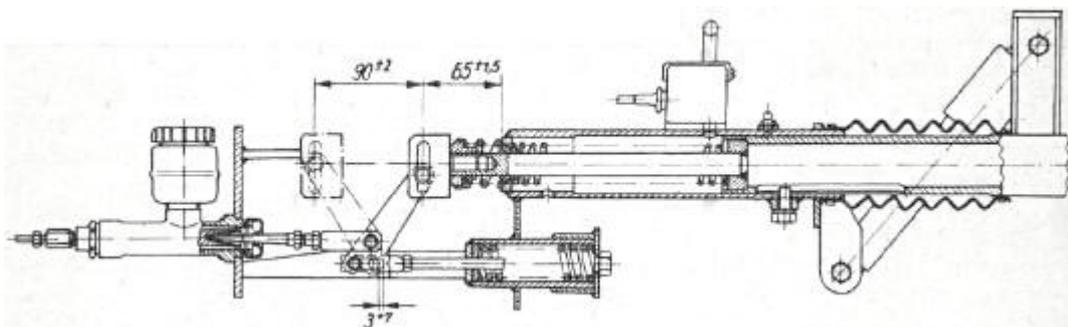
Mechanisch-hydraulisch wirkende Auflaufbremse des Bastei, des Intercamp HS sowie des Apolda Luxus im Schnitt
